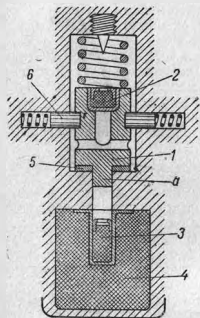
Ударный механизм взрывателя полупредохранительного типа:
